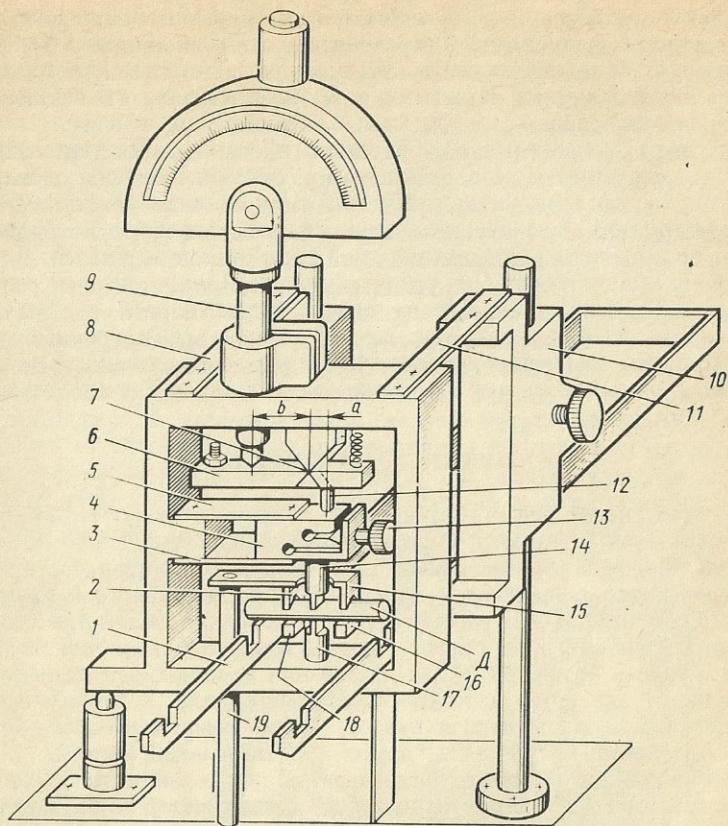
Измерительная оснастка для контроля цилиндрических деталей по диаметральным размерам
